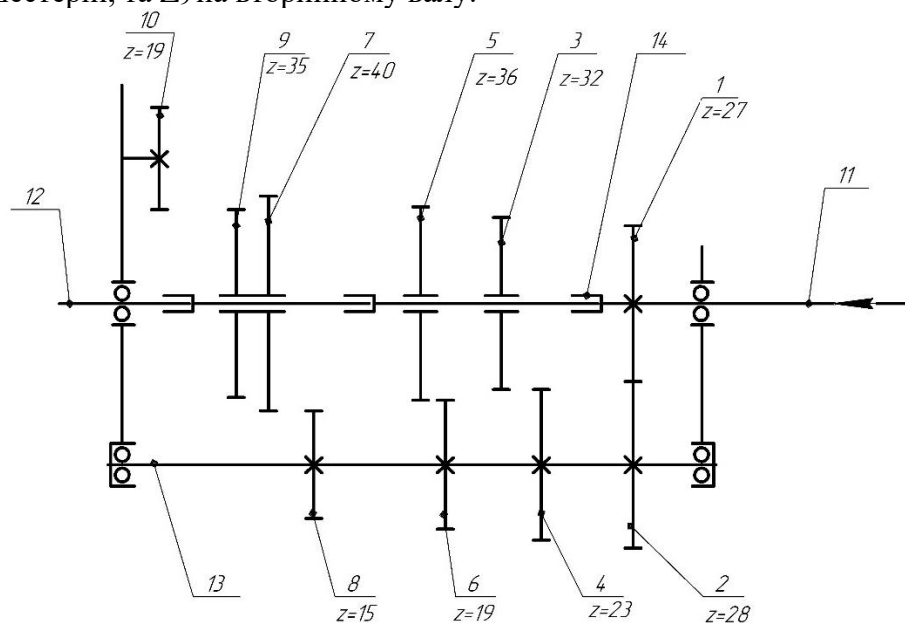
Кінематична схема стандартної коробки передач EatonFuller OT-11608
